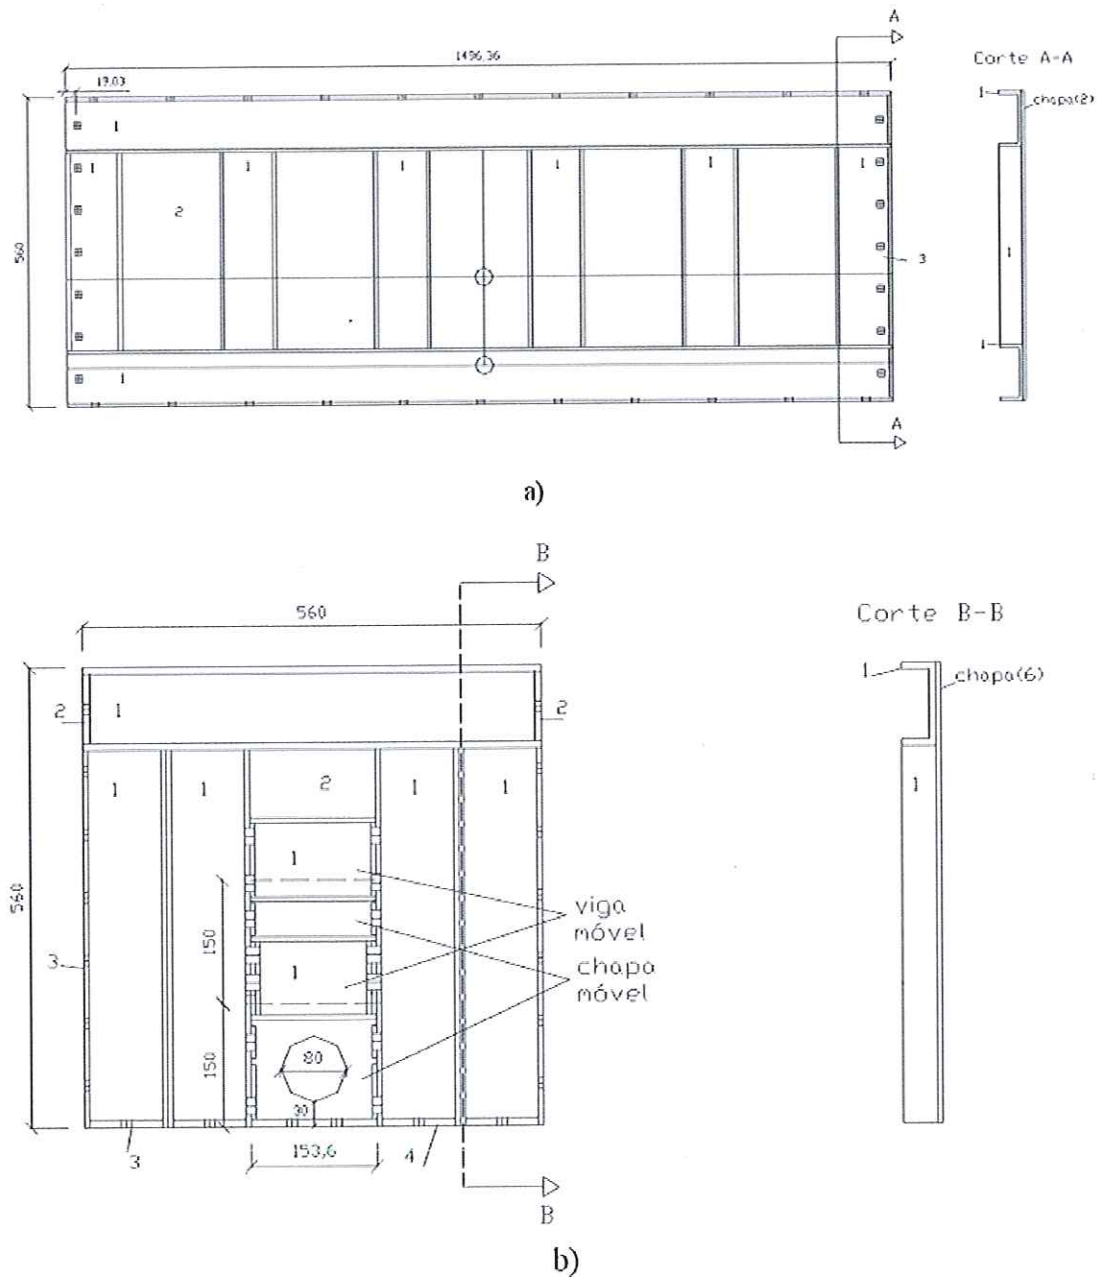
Detalhes do projeto da caixa de testes: a) parede lateral; b) parede frontal
